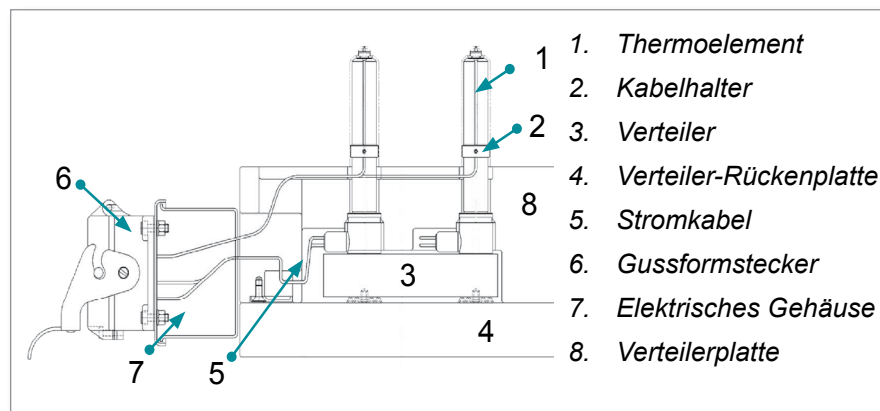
Thermoelement-Layout – Seitenansicht
